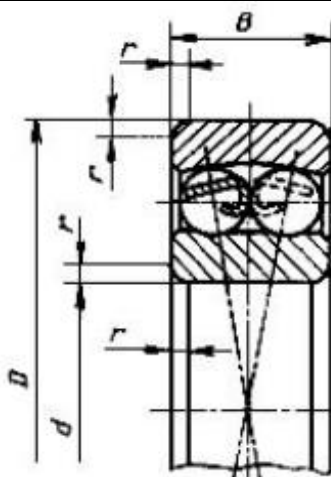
Размеры подшипника. Тип 1000 – с цилиндрическим отверстием внутреннего кольца
